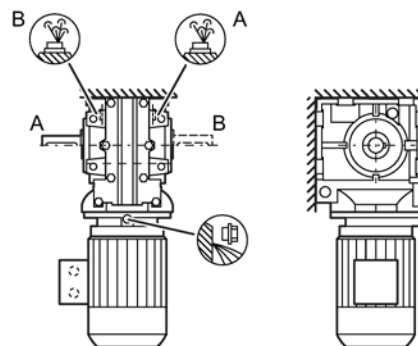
Монтажные положения для цилиндрического косозубого редуктора CF в исполнении с фланцем и CAZ с фланцем корпуса, типоразмеры 39- 89
